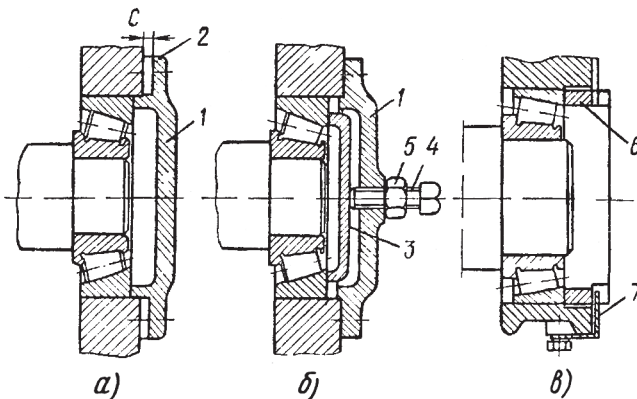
Схемы регулирования зазора в конических роликоподшипниках:
